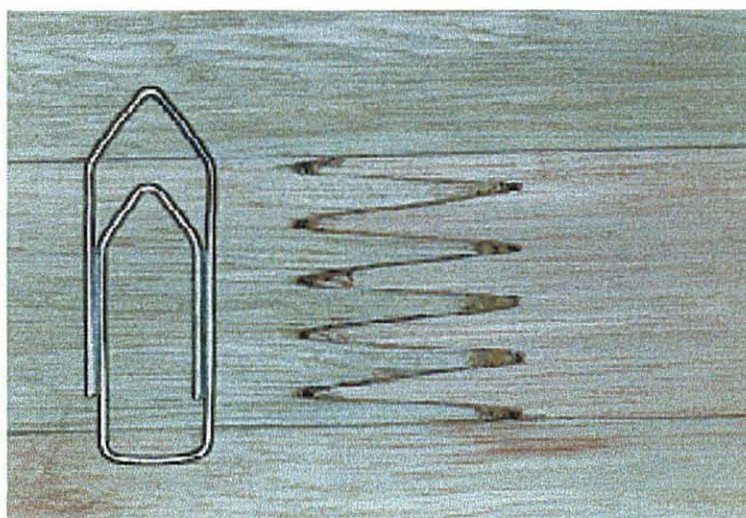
ENCAIXE LONGITUDINAL TIPO “FINGER JOINT” NAS PEÇAS DE MADEIRA
